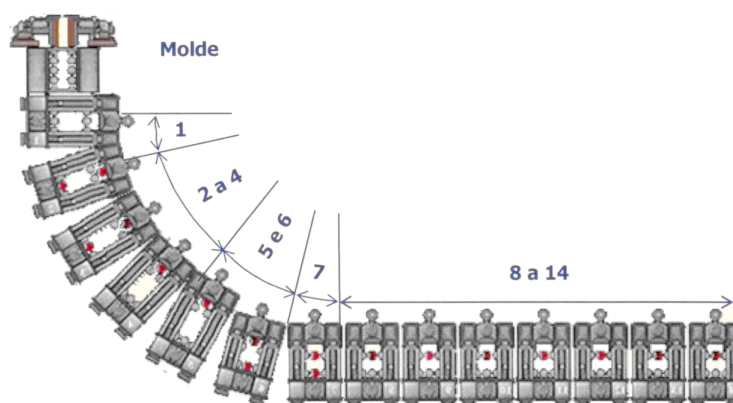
Identificação da posição do molde e segmentos 1 a 14 da máquina de Lingotamento Contínuo.
